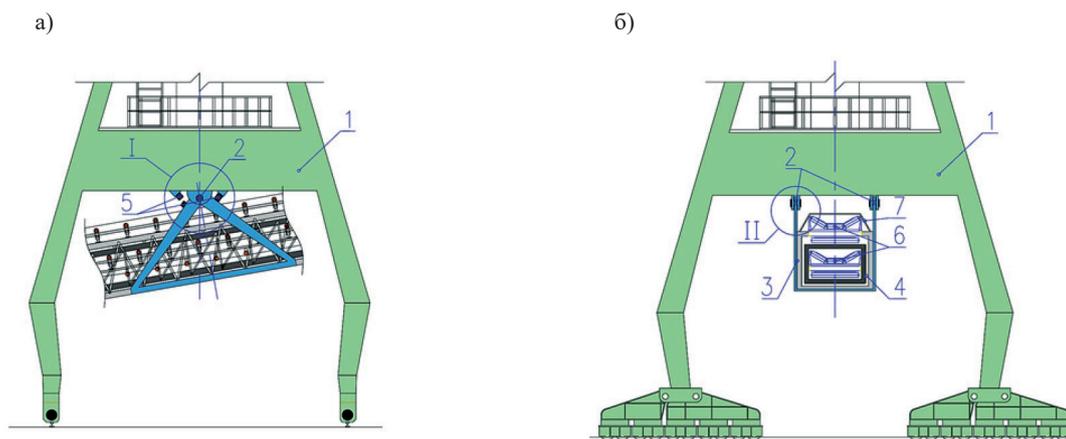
Конструкция шарнирного крепления неподвижной секции к portalу:
